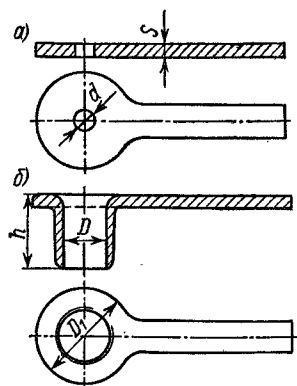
Отбортовка с утонением: а — заготовка; б — деталь
